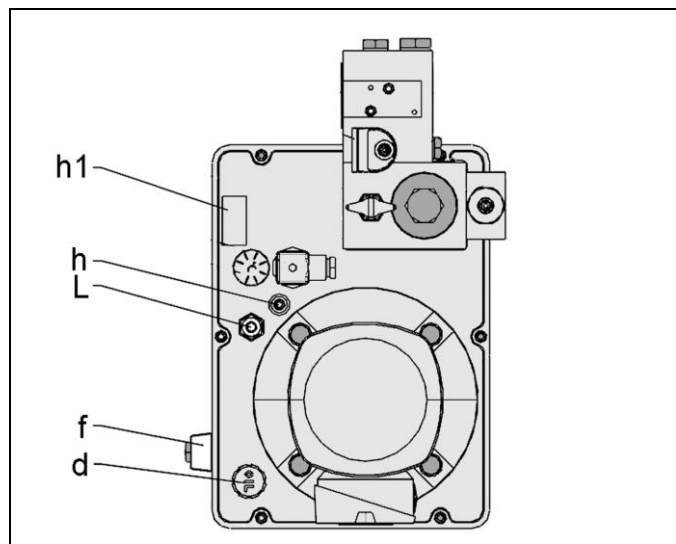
Illustration du couvercle du groupe hydraulique V11
